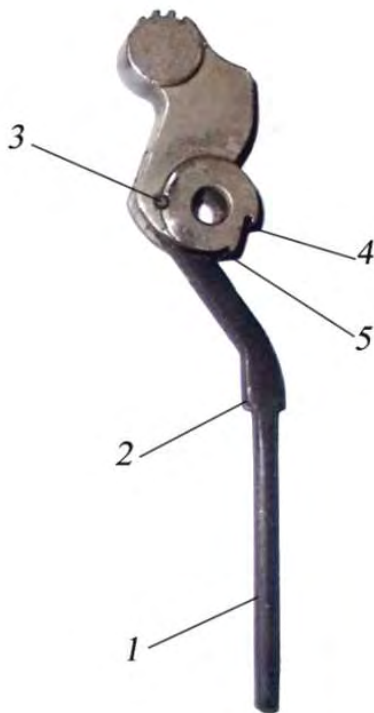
Курок с тягой курка: 1 – направляющий стержень боевой пружины; 2 – уступы; 3 – штифт; 4 – предохранительный взвод; 5 – боевой взвод
